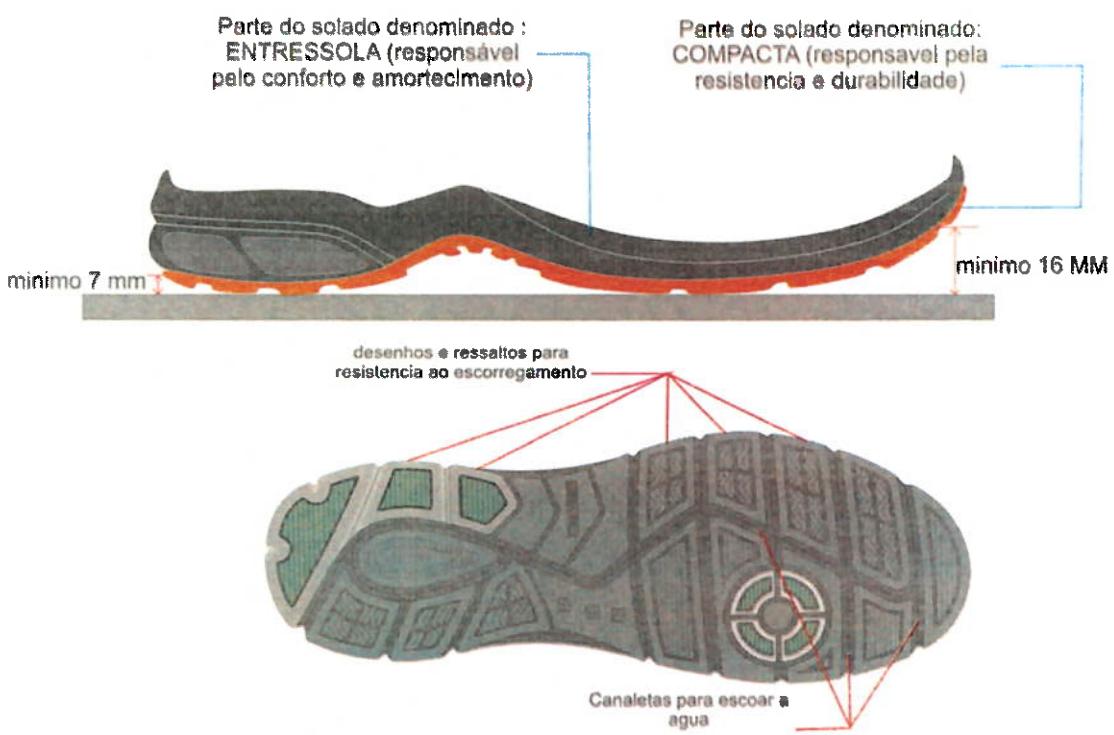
PERFIL E PLANTA DO SOLADO
